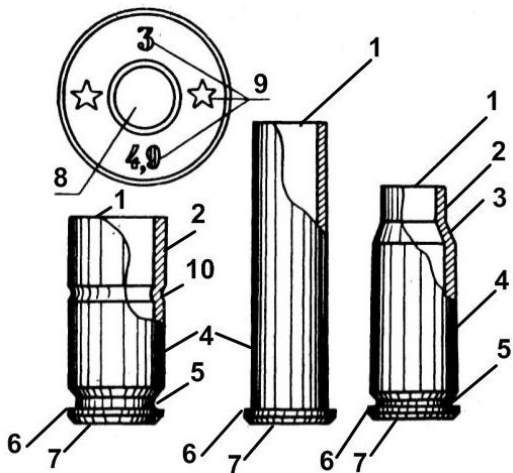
Части гильзы: 1) срез; 2) дульце; 3) скат; 4) корпус; 5) кольцевая проточка; 6) фланец; 7) доньшко; 8) капсюль; 9) маркировочные обозначения; 10) каннелюра
